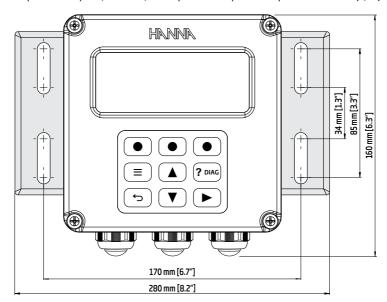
Panel para montaje en la pared, dimensiones de las ranuras
